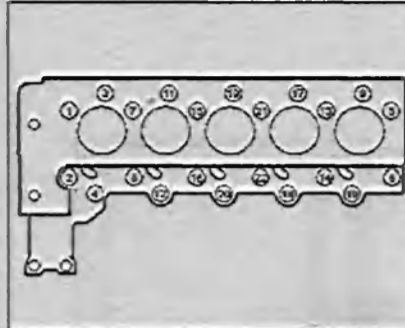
Порядок откручивания болтов крепления головки блока цилиндров.
